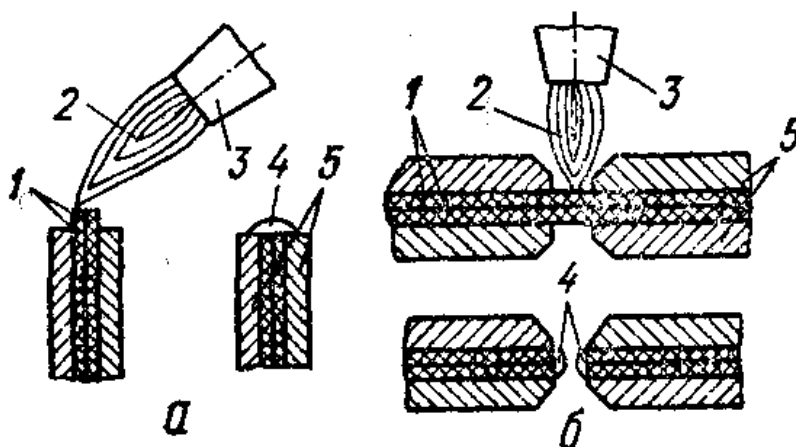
Схема зварювання плівок оплавленням (а - з підготовкою кромки, б - без підготовки кромки): 1-плівки; 2-струмінь газу; 3-наконечник нагрівача; 4-шов; 5-затискачі.
